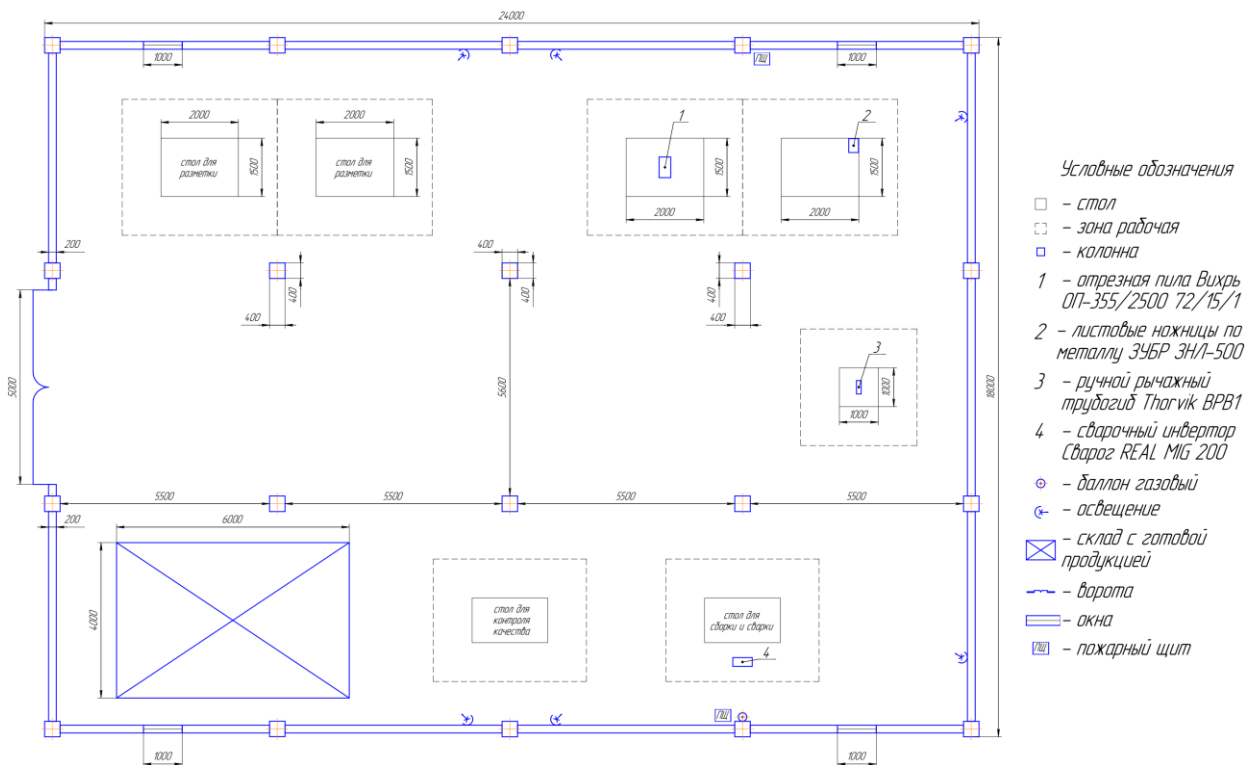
Планировка участка для сборки и сварки напольной вешалки для малых помещений
